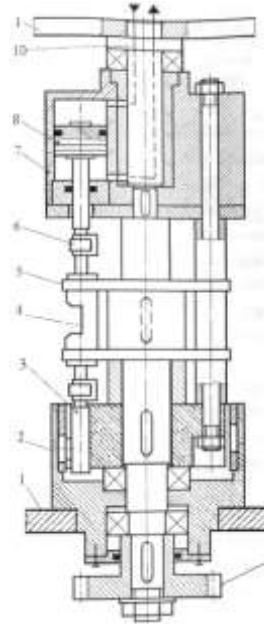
Типова конструкція технологічного ротора з комбінованим приводом: 1 – станина; 2 – блок нижніх повзунів; 3 – повзун; 4 – інструментальний блок; 5 – блокотримач; 6 – муфта; 7 – блок верхніх повзунів; 8 – гідроциліндр; 9 – зубчасте колесо
